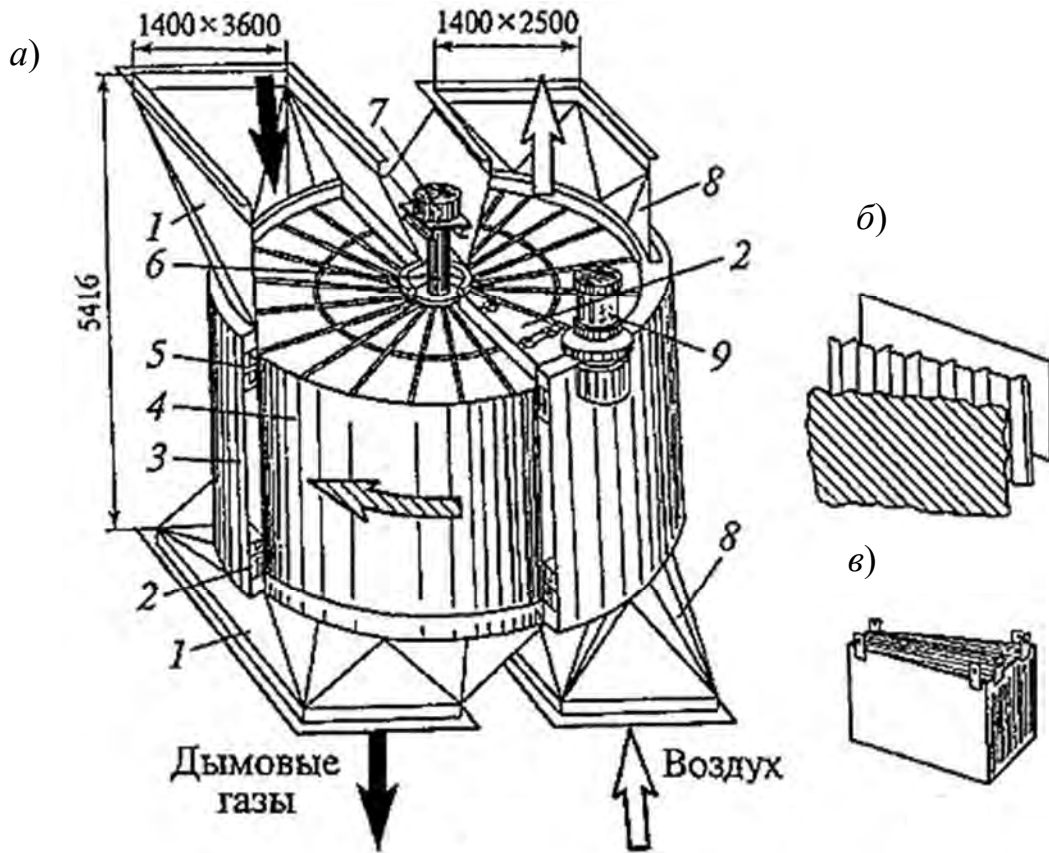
Регенеративный воздухоподогреватель: *a* – общий вид: 1 – газовые патрубки; 2, 5 – радиальное и периферийное уплотнения; 3 – наружный кожух; 4 – набивка; 6 – вал ротора; 7 – верхний и нижний подшипники; 8 – воздушные патрубки; 9 – электродвигатель; *б* – отдельные пластины различной формы; *в* – секция с пластинами
